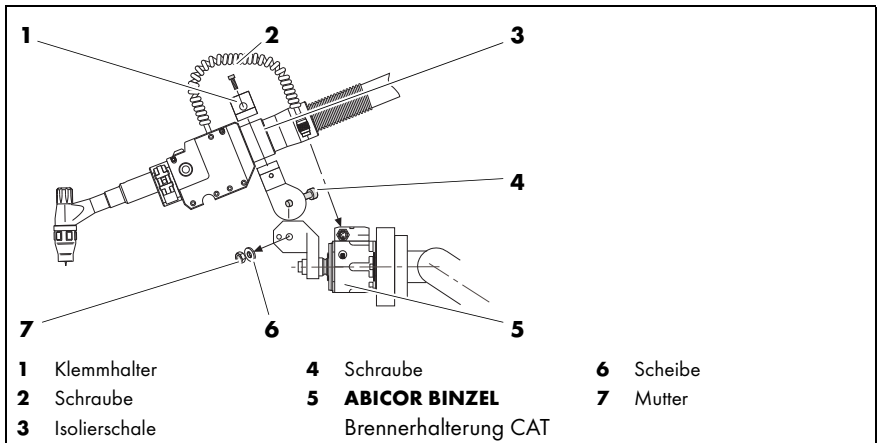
WIG-Schweißbrennersystem am Roboter montieren
